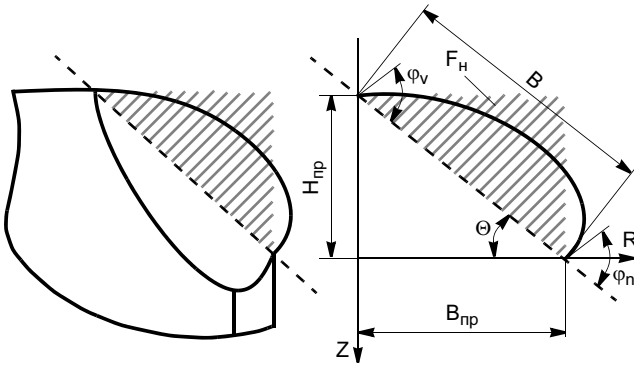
Схема формирования свободной поверхности сварочной ванны
